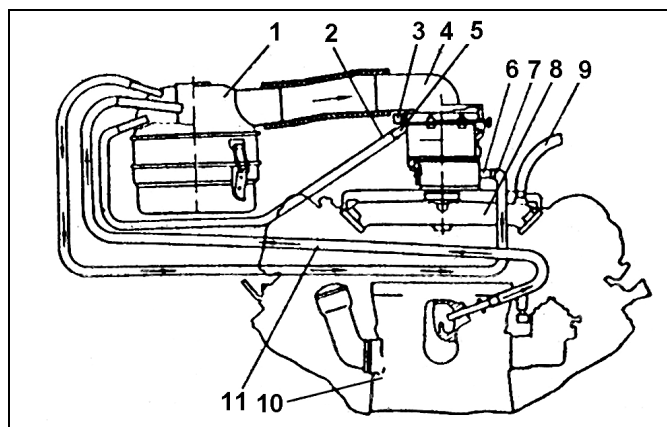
Схема отсоса картерных газов и разбалансировки поплавковой камеры карбюратора: 1 - воздушный фильтр; 2 - шланг разбалансировочный поплавковой камеры карбюратора; 3 - шланг от топливного насоса; 4 - карбюратор; 5 - соединительная трубка клапана стояночной разбалансировки поплавковой камеры; 6 - патрубок отсоса картерных газов в карбюратор; 7 - шланг отсоса картерных газов из воздушного фильтра в карбюратор; 8 - впускной коллектор; 9 - шланг к гидраввакуумному усилителю; 10 - крышка распределительных шестерен; 11 - шланг отсоса картерных газов.
